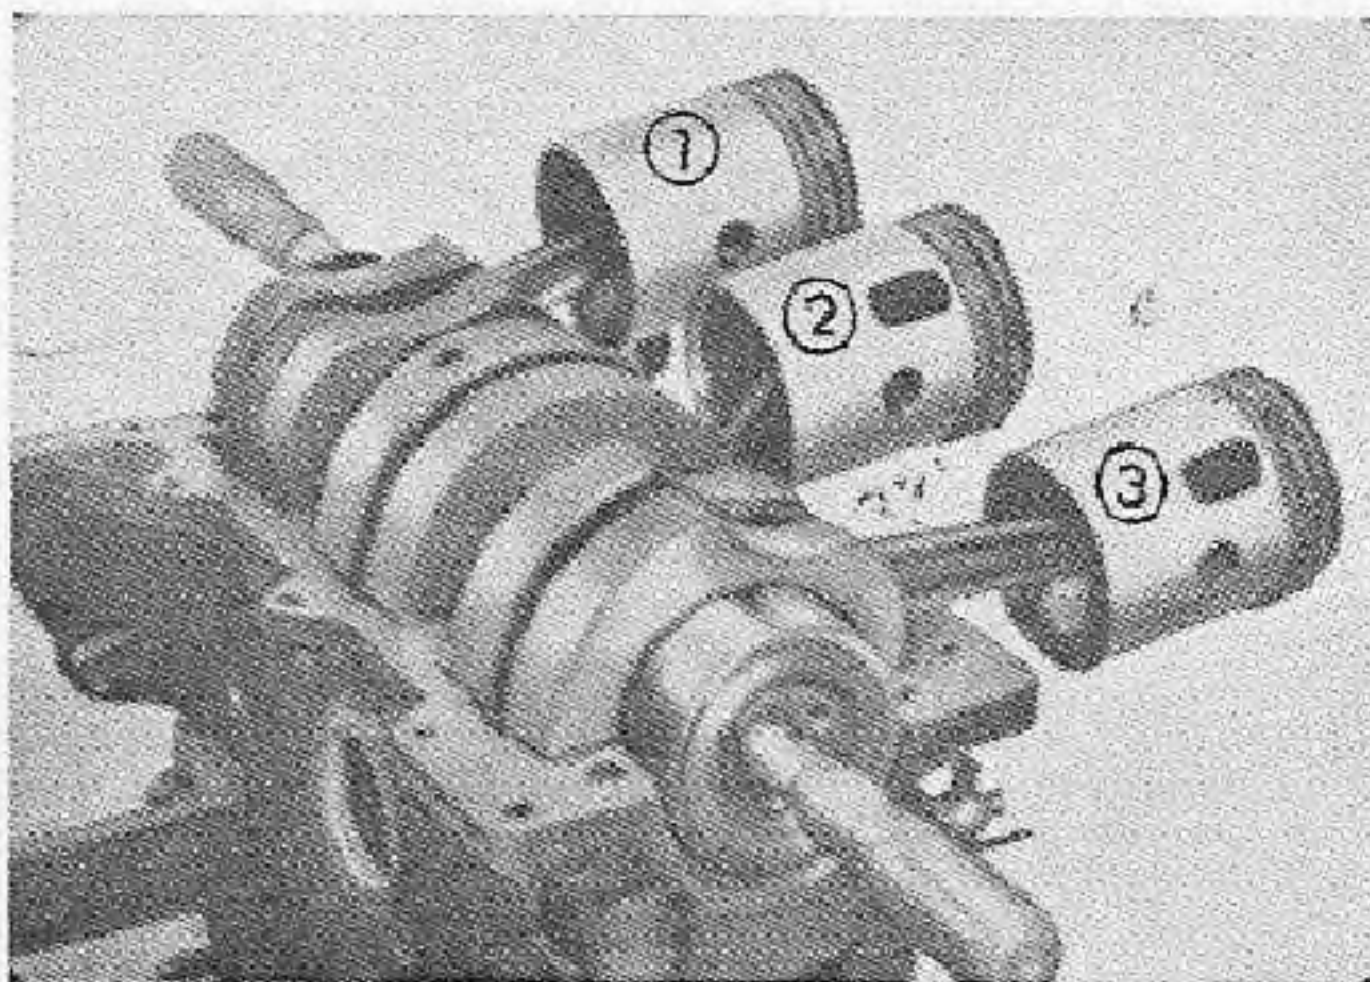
El cigüeñal colocado sobre el block, para proceder al desmontaje de los pistones.
